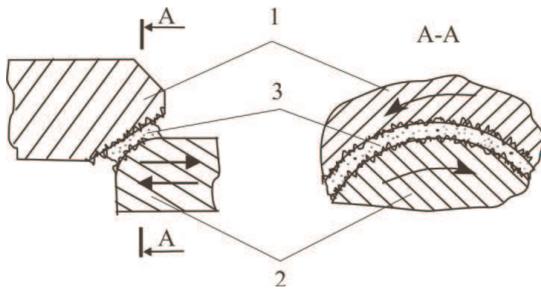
Схема контактной зоны условно неподвижно соединяемых деталей, разделенных аморфным промежуточным слоем, при приложении сдвигающей нагрузки: 1 – охватывающая деталь, 2 – охватываемая деталь, 3 – промежуточный слой. Стрелками указаны векторы возможных осевых и крутильных колебаний деталей герметизирующего узла.
